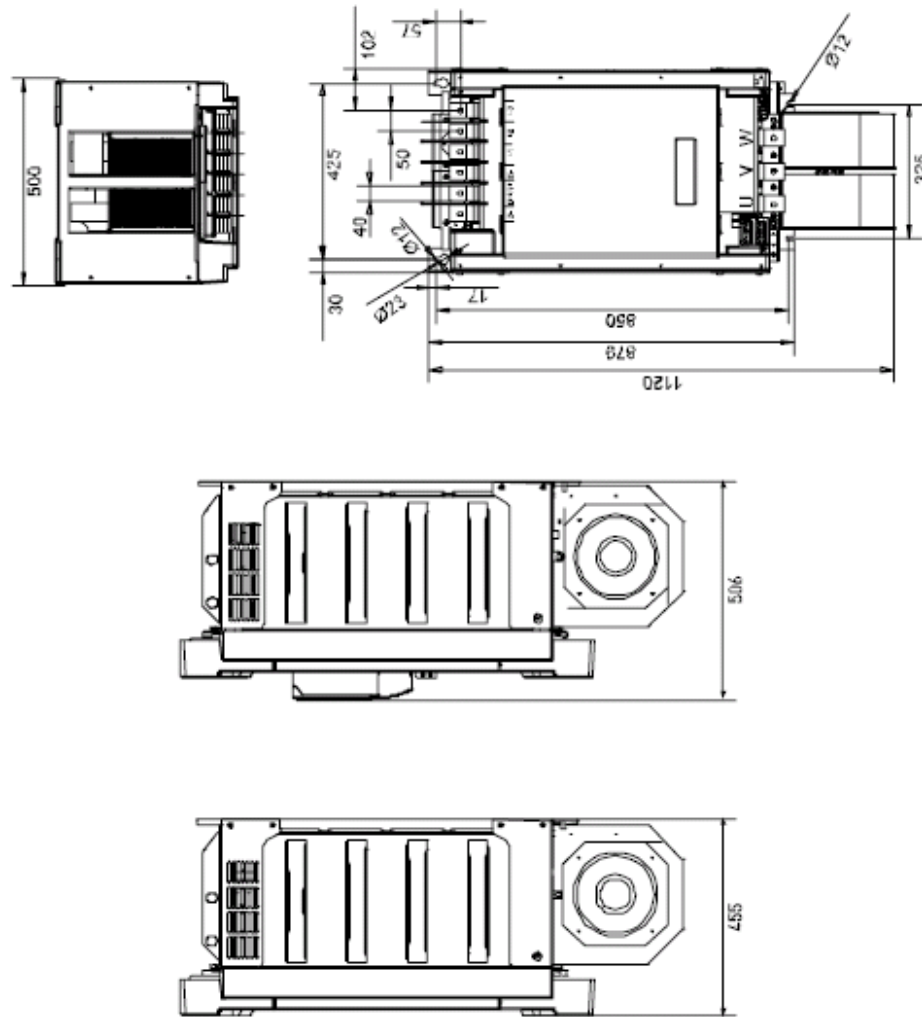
Габариты типоразмера FR10 (вес = 120 кг)
